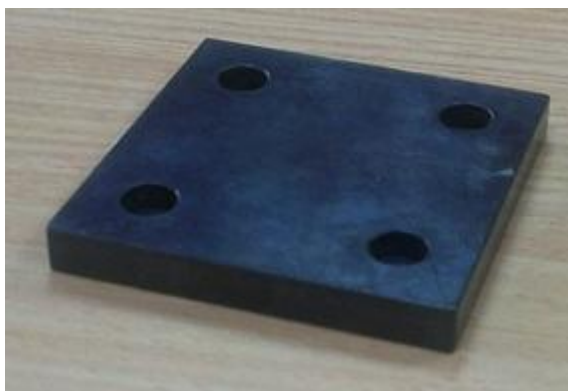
Общий вид меры-плоскопараллельной пластины
